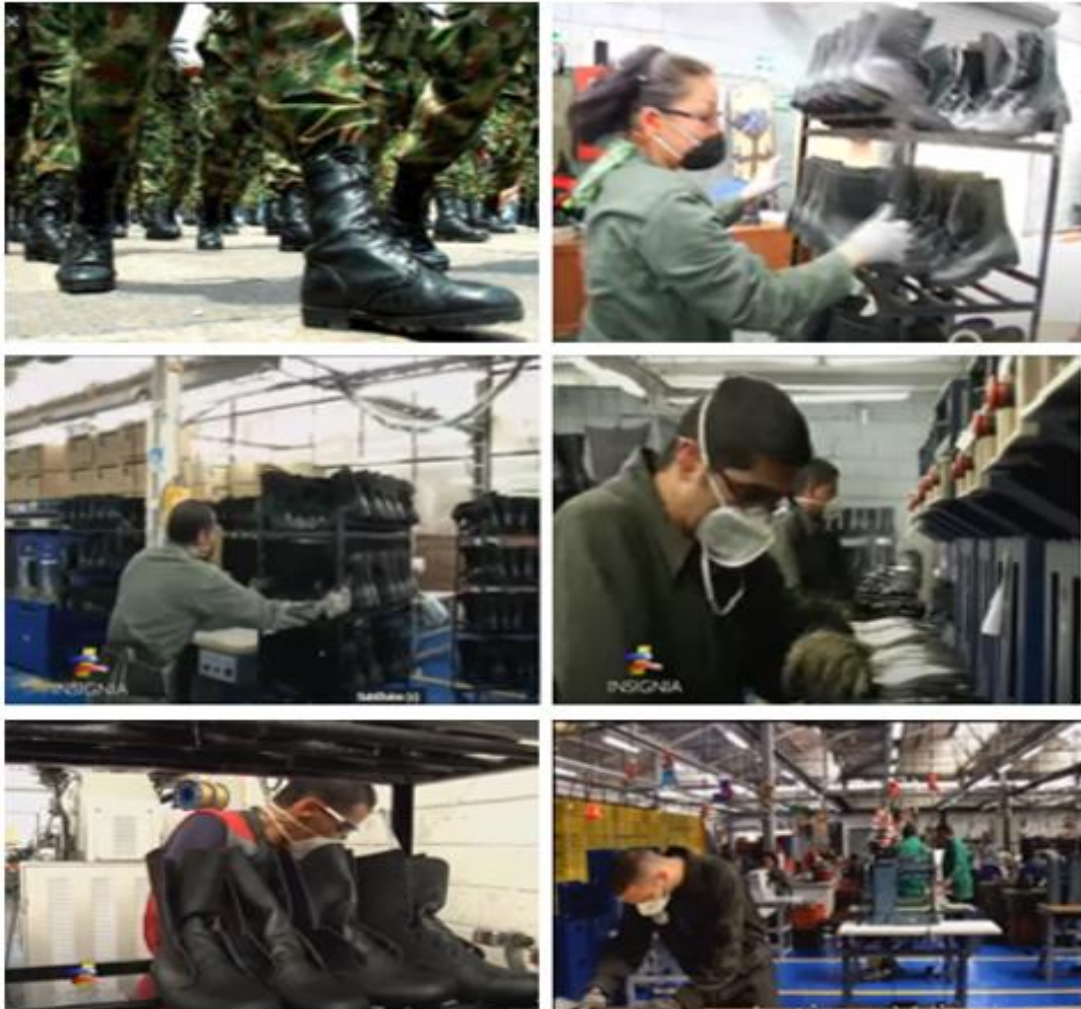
Proceso productivo planta de zapatería BAIN.T.
